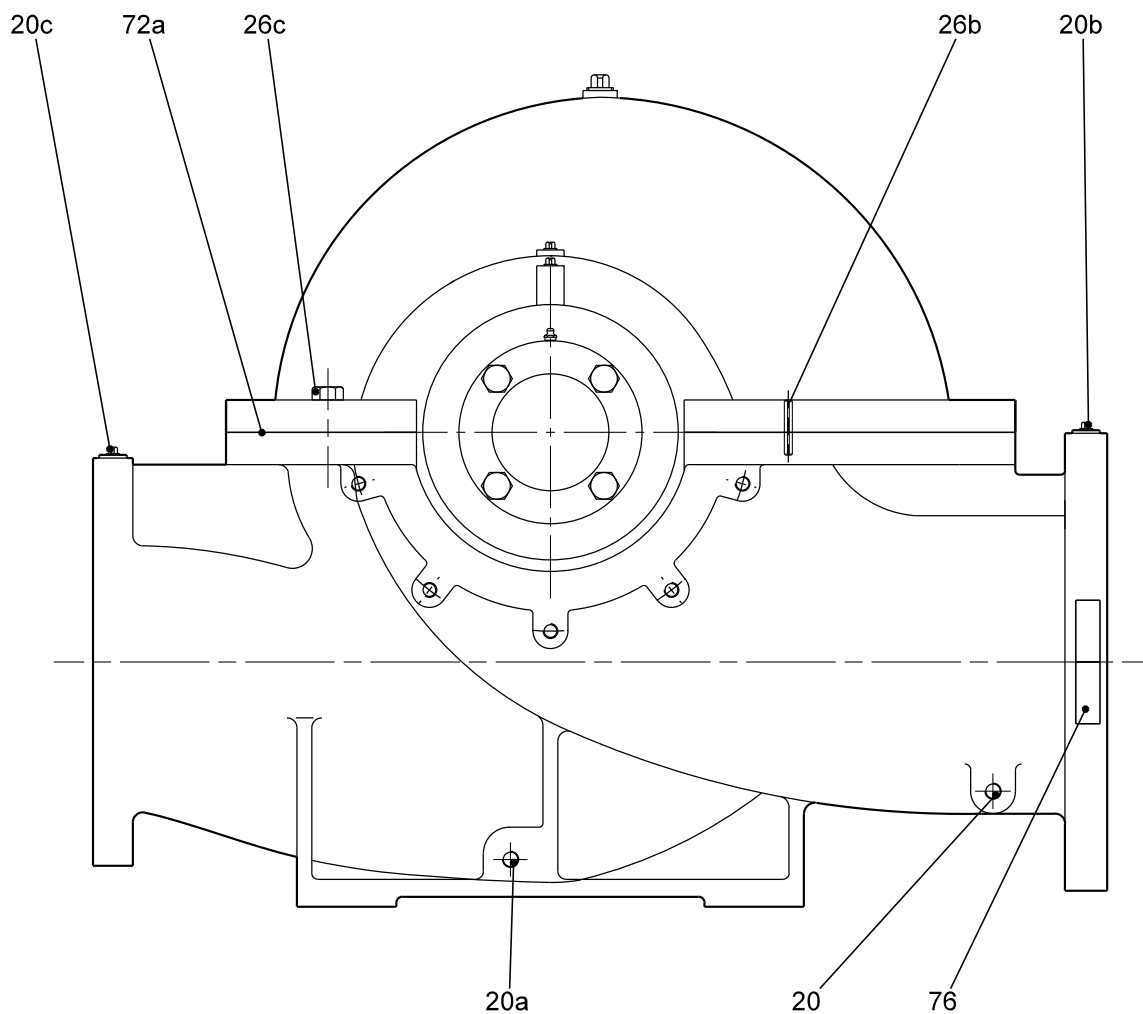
Вид в разрезе, тип конструкции 4, с торцевыми уплотнениями вала
